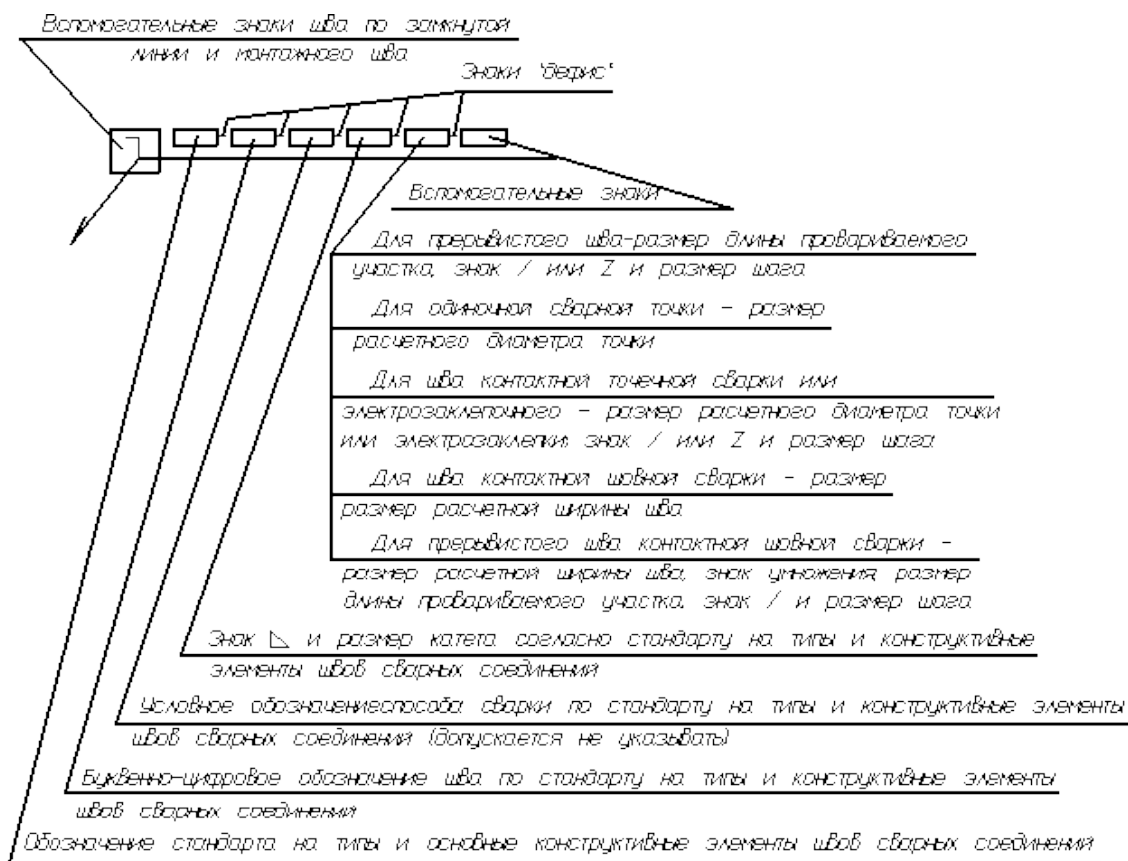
Расположение вспомогательных знаков в обозначении сварного шва
